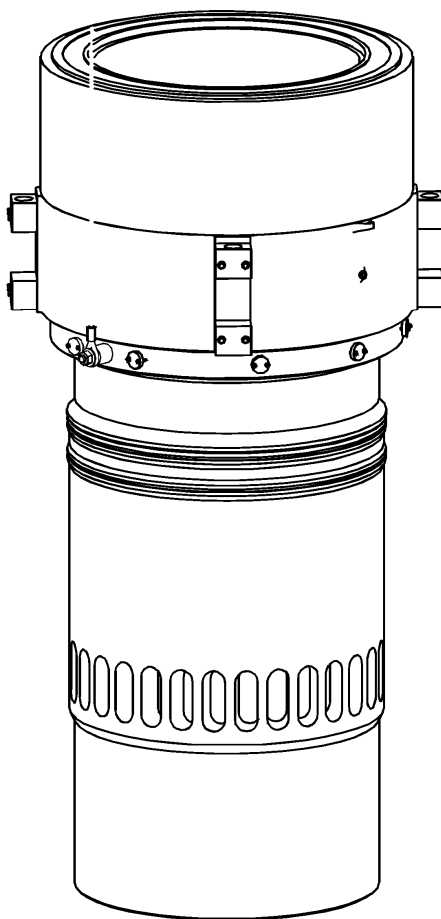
Втулка циліндра та охолоджуюча сорочка
